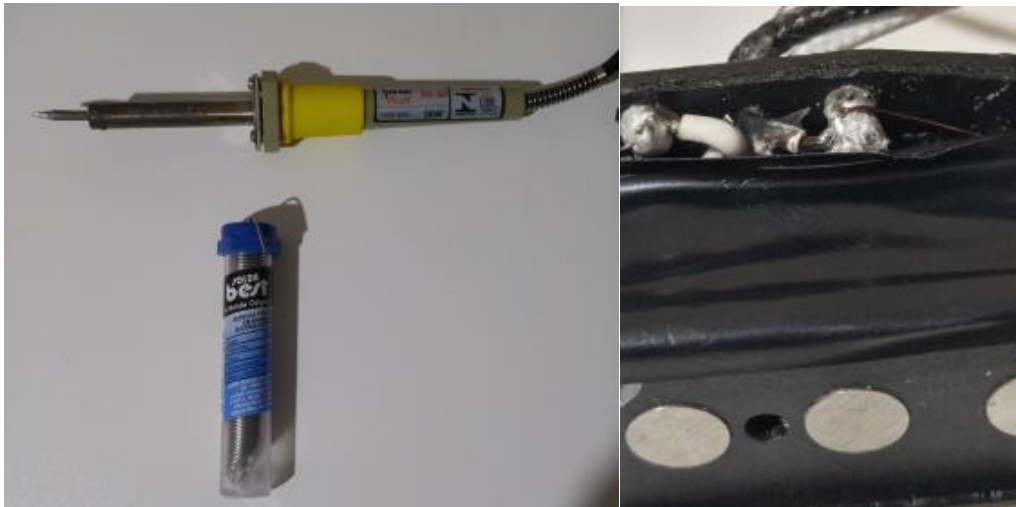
Ferro de soldar e solda à esquerda, e solda do captador enrolado com alumínio.
